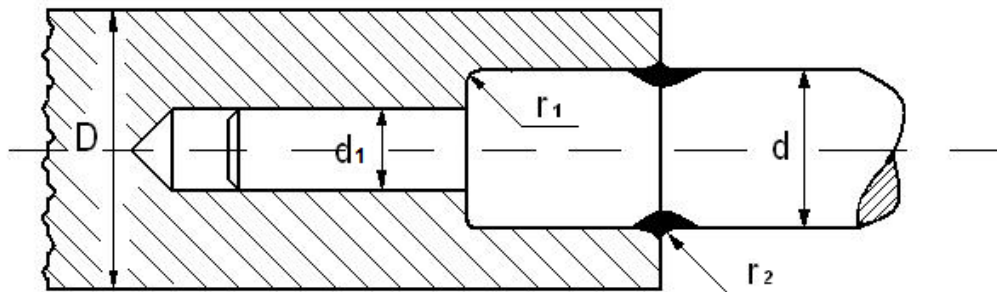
Esquema de la unión espigada y soldada.
